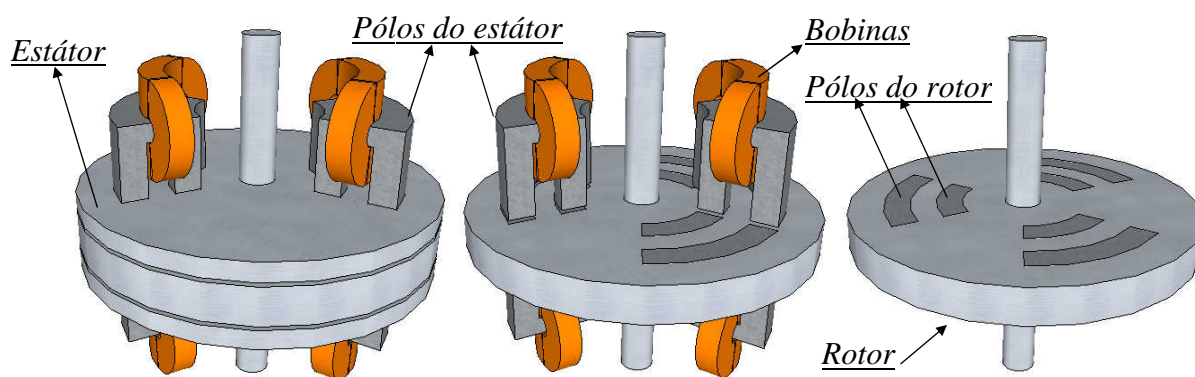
Máquina rotativa de fluxo axial bifásica.
